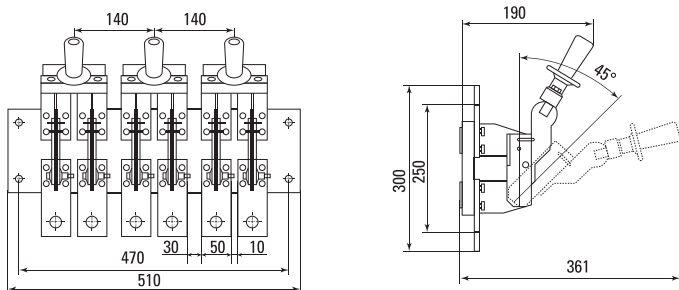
Габаритные и установочные размеры разъединителя типа PE19-44 с рукояткой для полюсного оперирования
